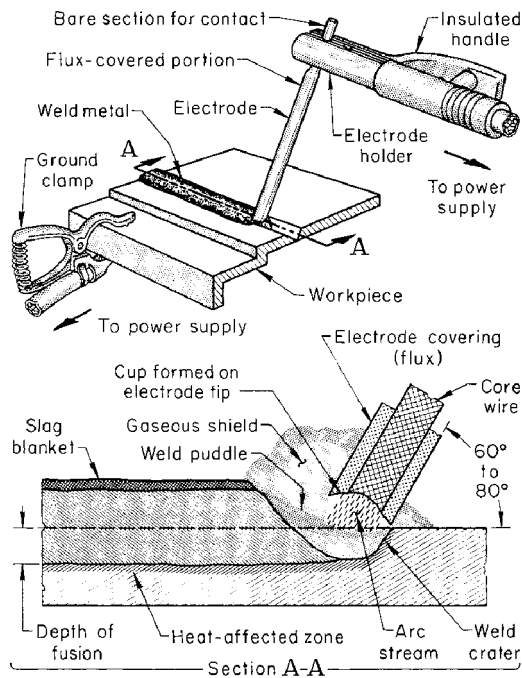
Saldatura elettrica con elettrodo rivestito.
